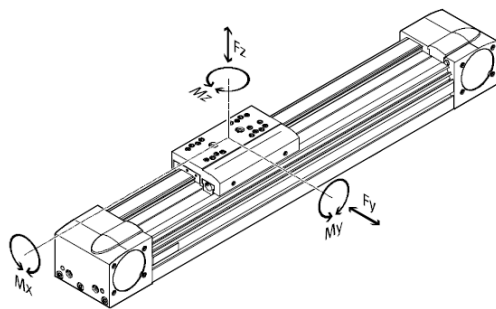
привод с зубчатым ремнем с шариковой направляющей.
